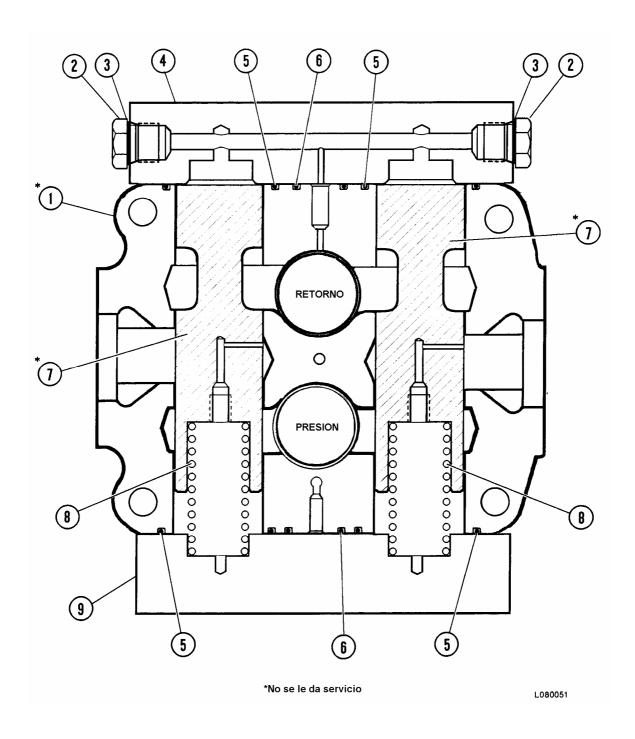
CONJUNTO DE LA SECCION DEL CARRETE DE LAS LUMBRERAS DEL ESTANQUE
